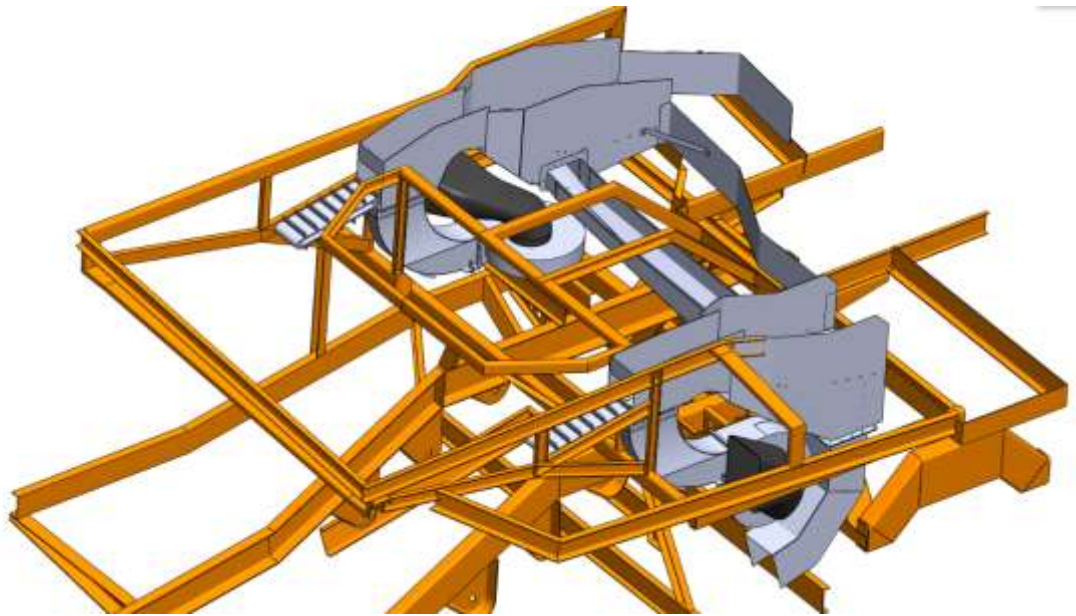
Detalle de colocación del conjunto separador. Notar las estructuras laterales que dan soporte al conjunto.
